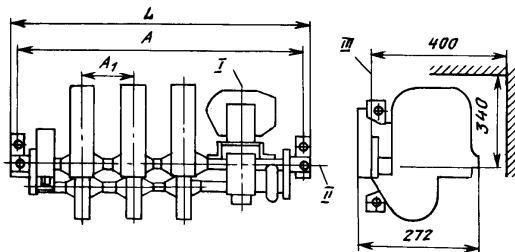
Габаритные и установочные размеры контакторов КТ6052 и КТ6053. Остальное - см. рис. 1
